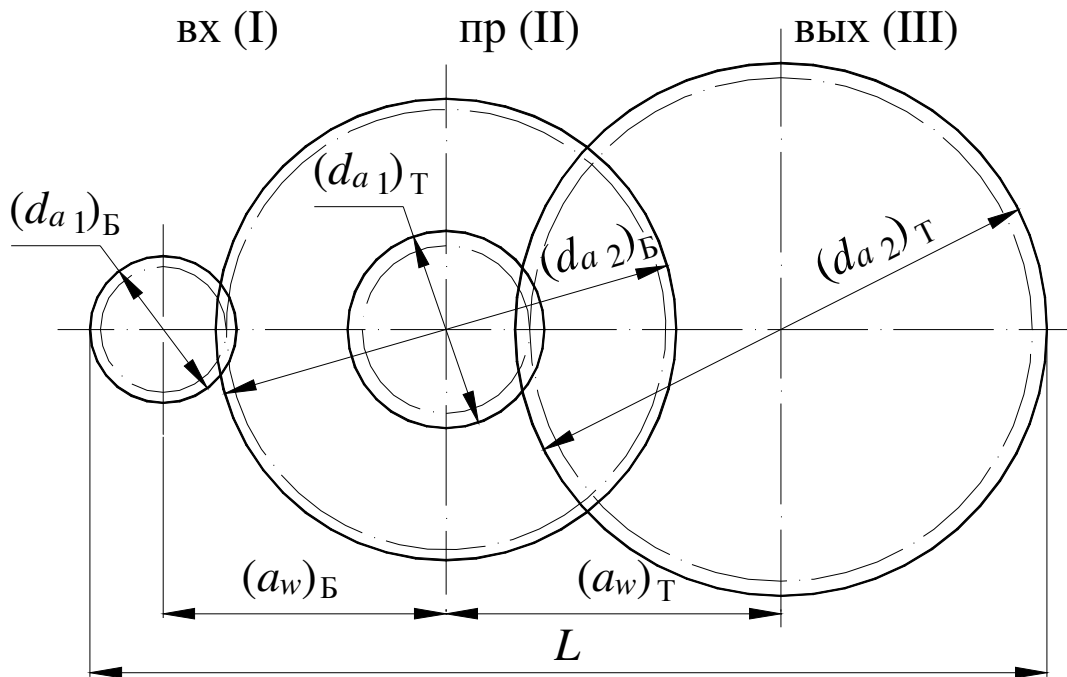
Комплект цилиндрических зубчатых колес:
